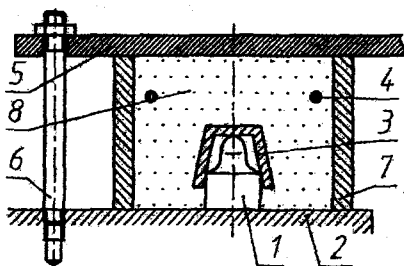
Схема штамповки взрывом в песке: 1 – пуансон; 2 – основание установки ВШ; 3 – заготовка; 4 – БВВ (кольцевой заряд); 5 – верхняя крышка; 6 – стяжные шпильки; 7 – разрушаемый (одноразовый) корпус; 8 – песчаная передающая среда
